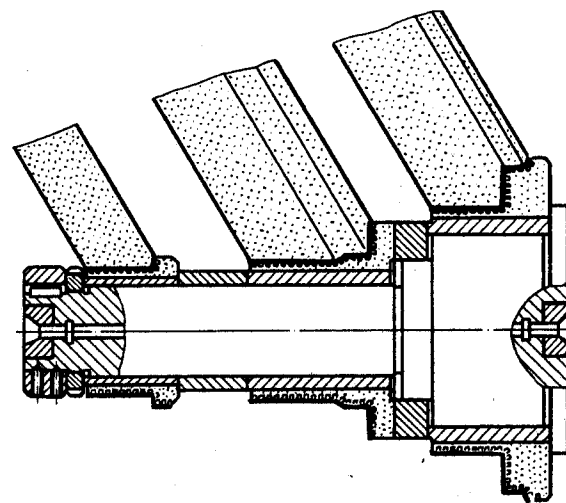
Схема правки рабочих поверхностей кругов алмазными роликами для многокругового шлифования разобнесенных поверхностей цапфы заднего моста автомобиля
